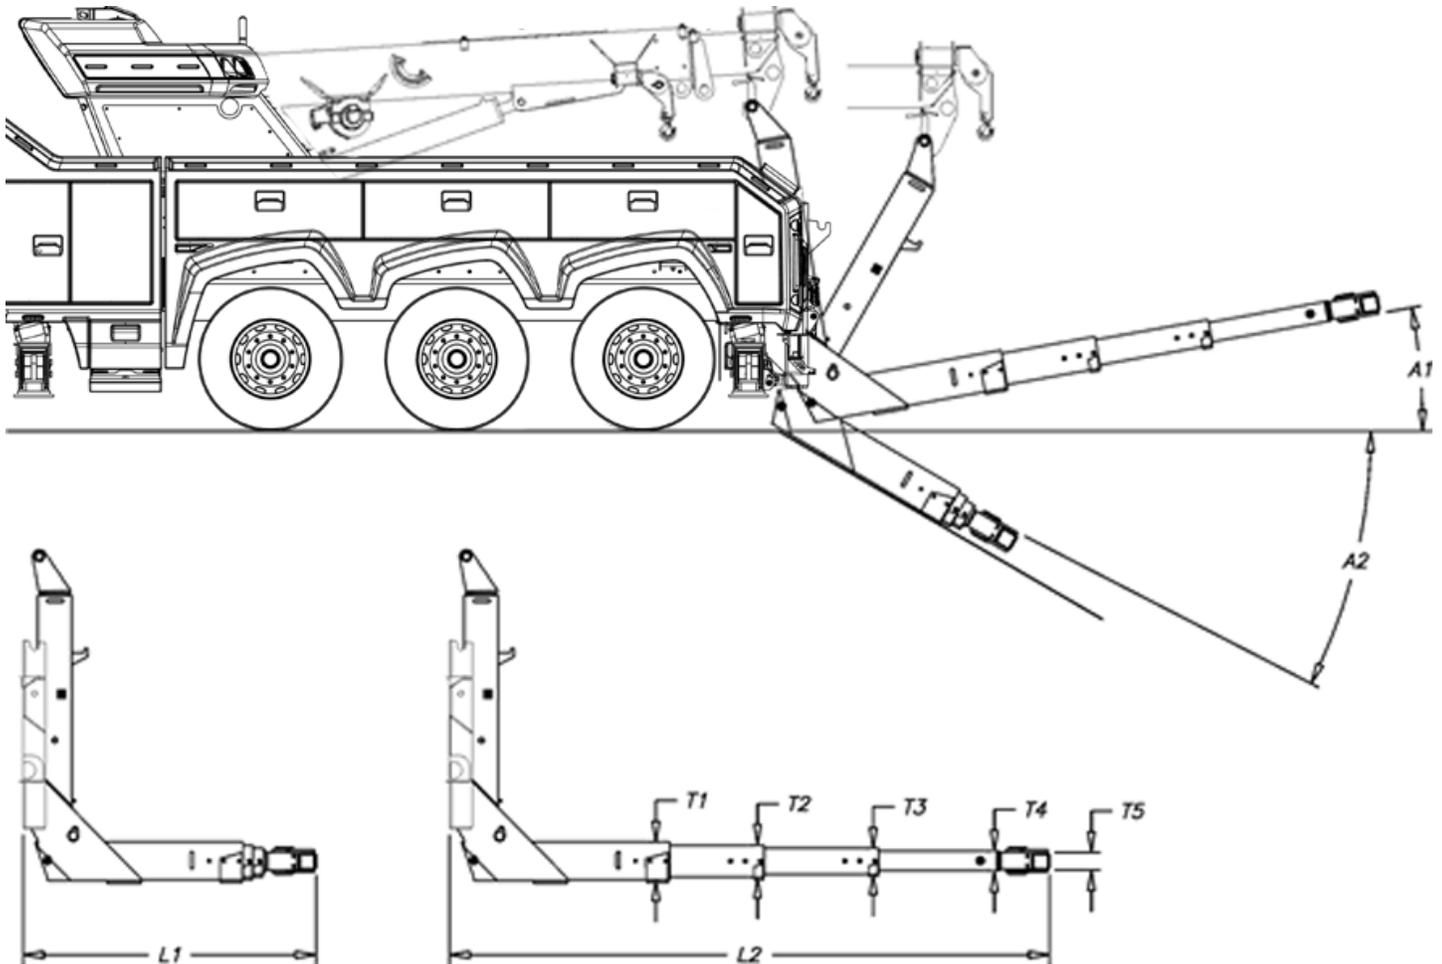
DIMENSIONS DU BRAS DE REMORQUAGE (EXEMPLE)
